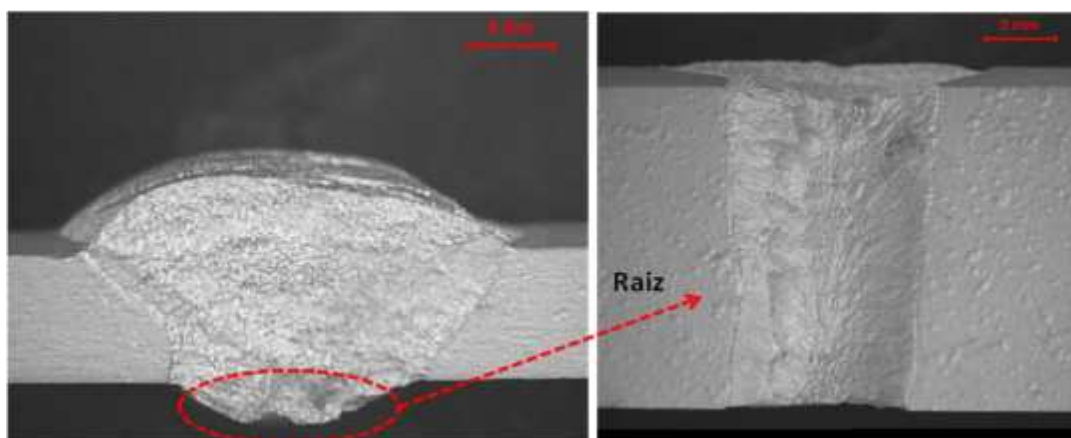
Aspecto macroscópico da raiz da solda, depois do ensaio, corpo de prova com solda – 05. Fonte: Do autor
